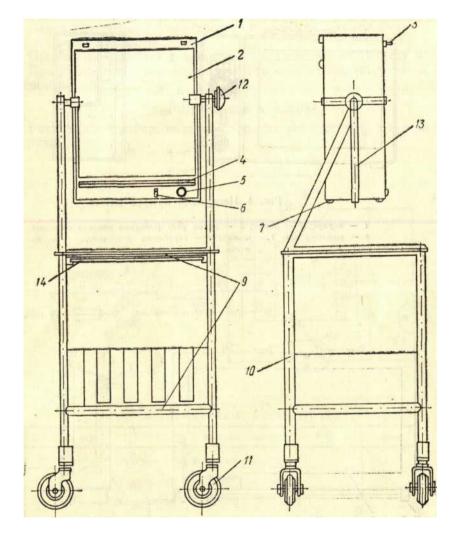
Негатоскоп общего назначения передвижной НТ-48. Общий вид /— кврпус; 2— экран; 3— кронштейн; 4— лоток; 5— ручка регулировки яркости; 6— выключатель; 7— ножка; 9— полка; 10— каркас; //— колесо; 12— ручкафиксатор; 13— рама.
